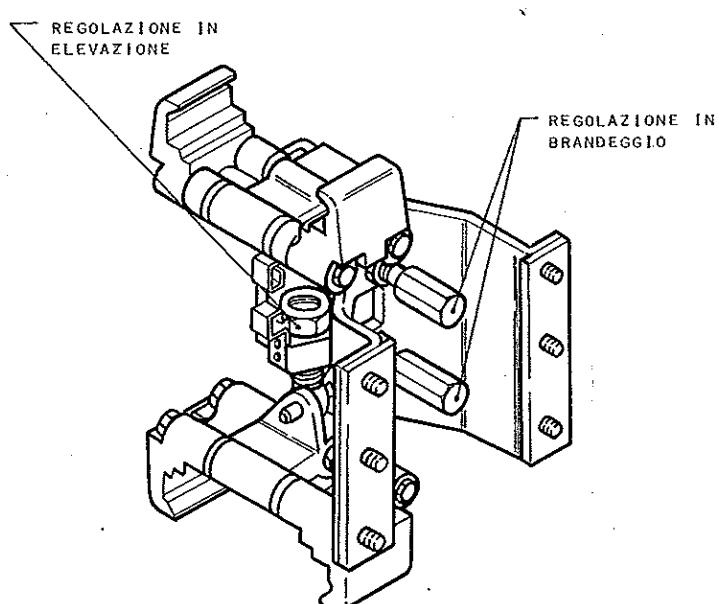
COLLIMAZIONE OTTICA DELLE ARMI SUL CAVALLETTO
